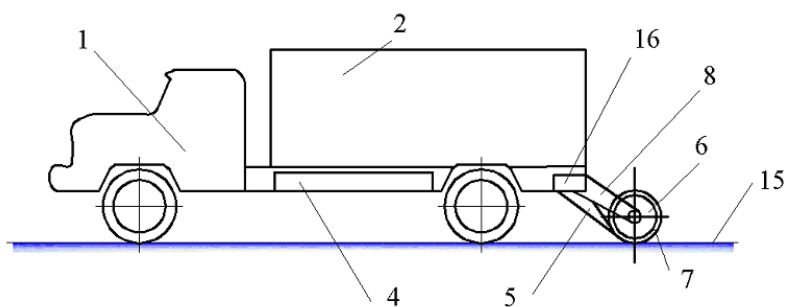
Машина с устройством для образования шероховатости на ледяной поверхности дороги
